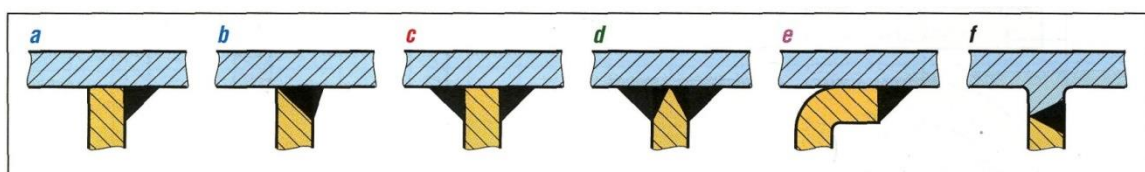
soudures en angle ou en T. Pour c et d, soudage des deux côtés.
